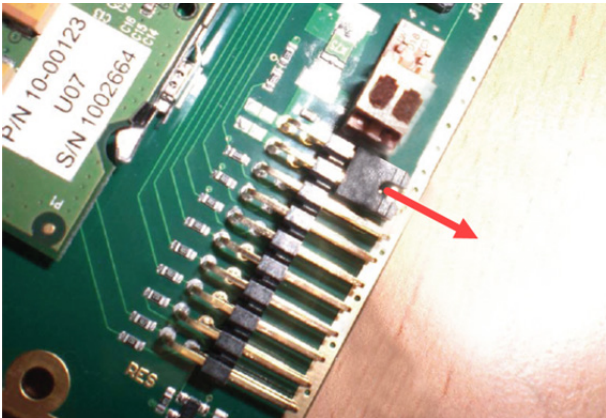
Entfernen des Jumpers für die Installation in ein Einschub-Chassis
